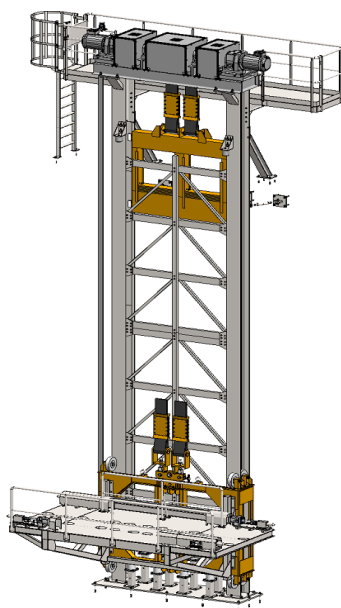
Elevador, Conjunto Geral do equipamento [20]
